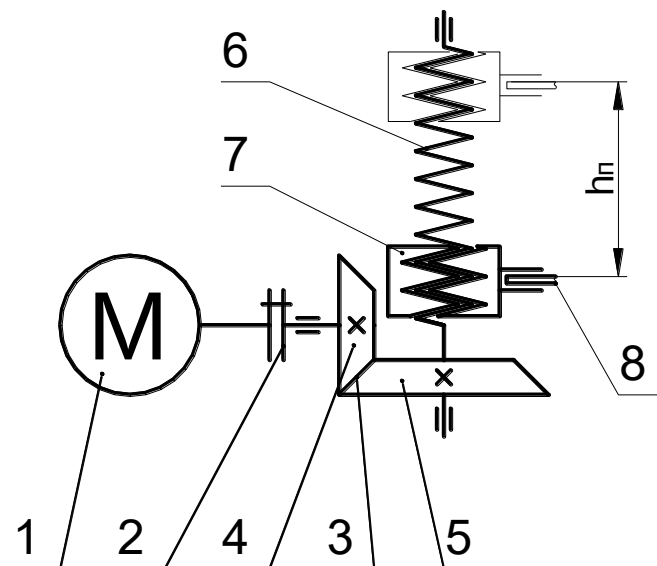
Механізм приводу підйомника: 1 – електричний двигун; 2 – муфта; 3 – зубчастий конічний редуктор; 4 – конічна шестерня; 5 – конічне колесо; 6 – ходовий гвинт; 7 – гайка; 8 – платформа
